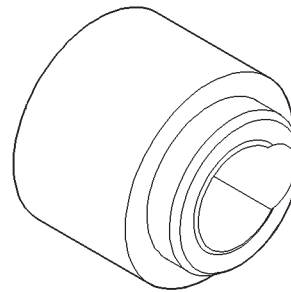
Ausbauwerkzeug C-4129-A für Hydrostößel
